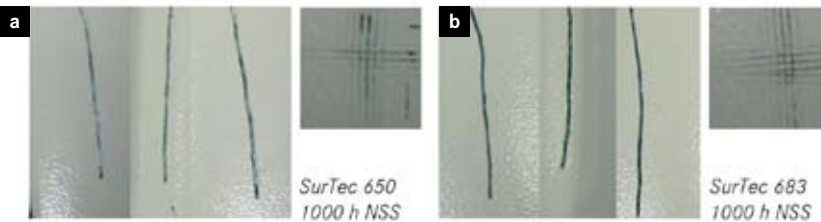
a) Passivierung für Aluminium und Zink, b) Standardpassivierung
